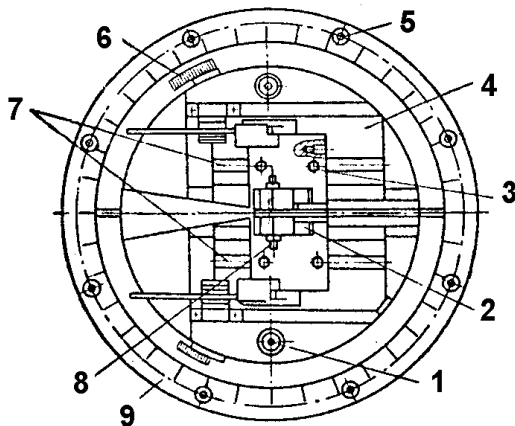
Люлька: 1 – валик для разворота суппортов на угол конусности зуба; 2 – резцедержатель; 3 – винт закрепления резцедержателя; 4 – суппорт; 5 – гайки зажима поворотного сегмента; 6 – шкала; 7 – пазы для закрепления суппортов; 8 – винт для закрепления резца; 9 – шкала для контроля угла качания люльки
